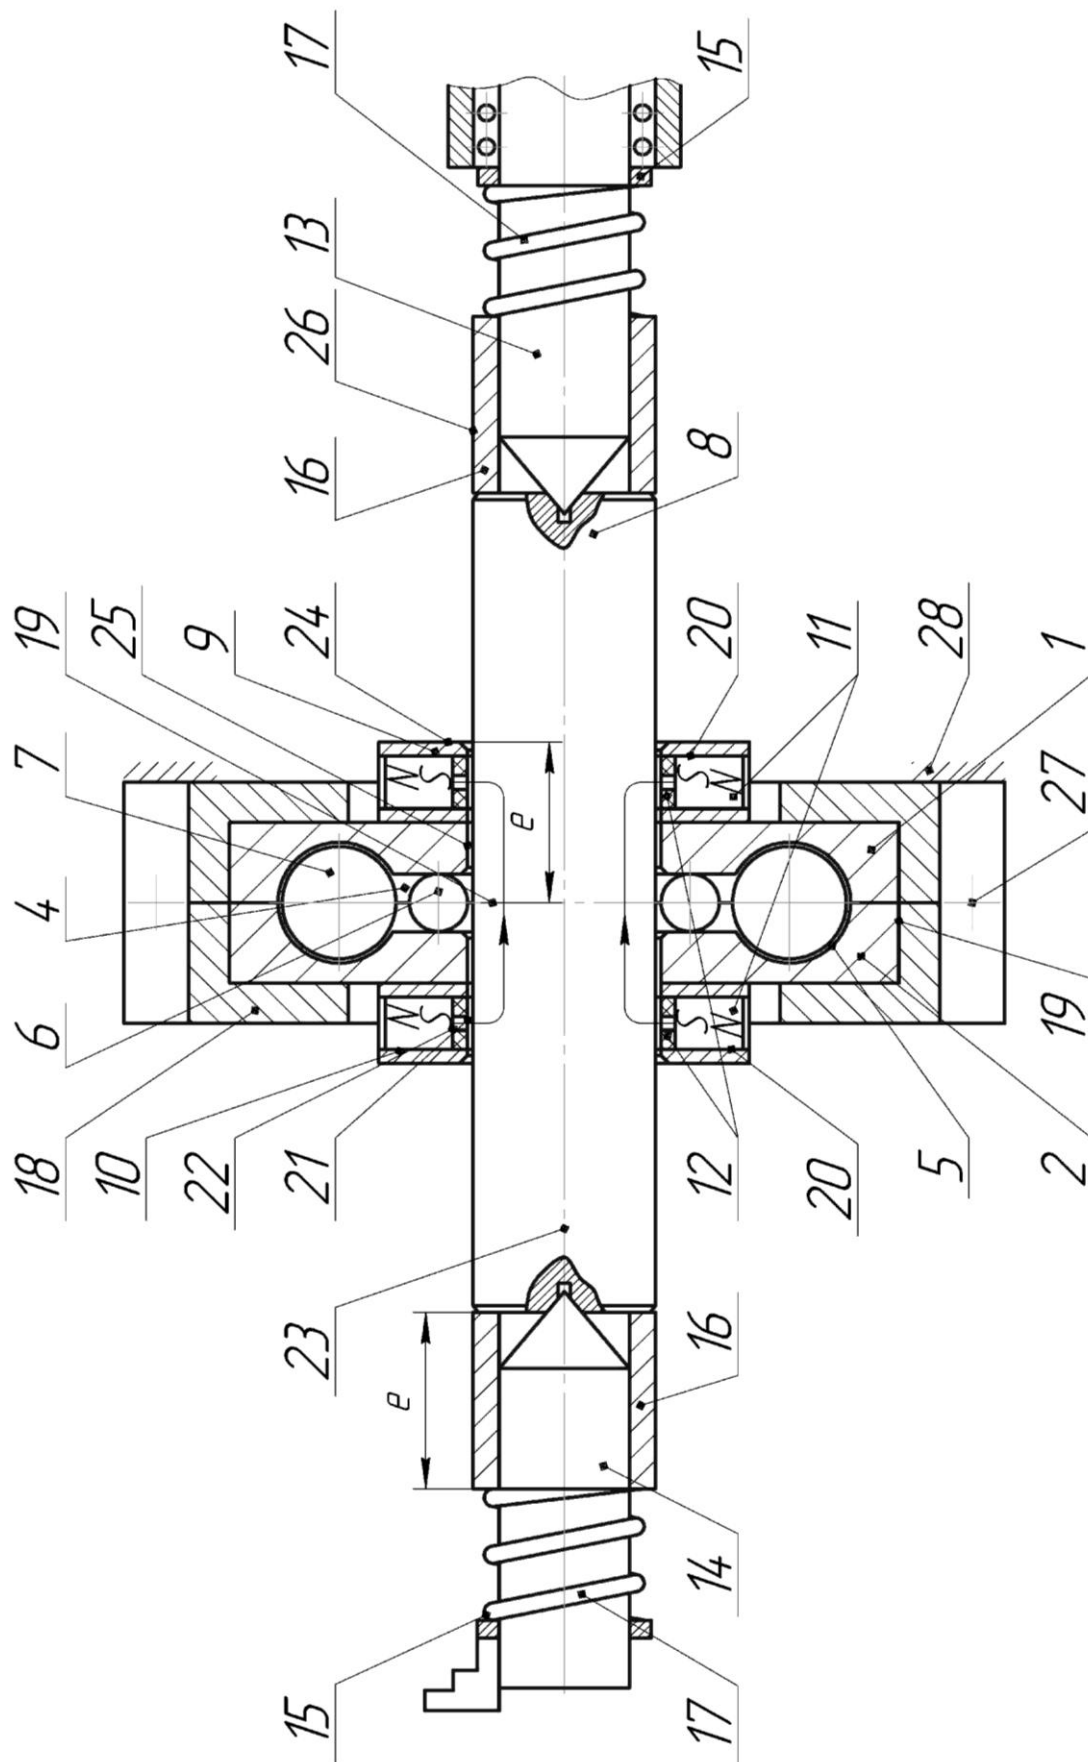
Конструкция устройства для магнитно-динамического упрочнения поверхности вала
